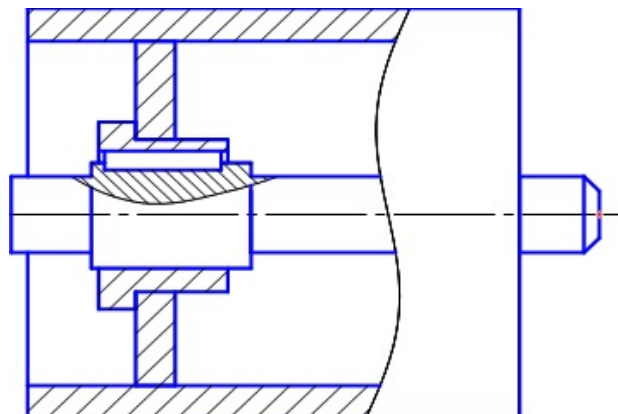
Изображение сварного изделия на сборочном чертеже
